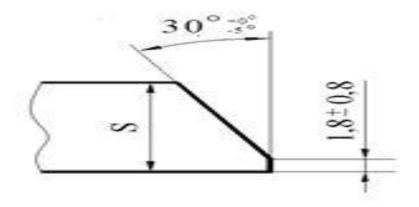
Подготовка кромок сварного соединения С17 под сварку
